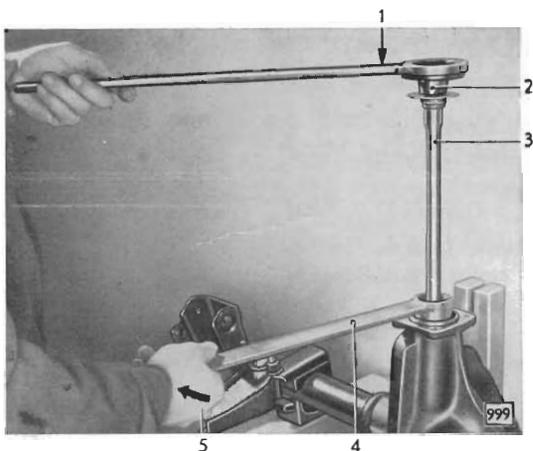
Lagerspiel des Antriebkegelrades durch Anziehen der Nut- bzw. Sechskantmutter beseitigen
